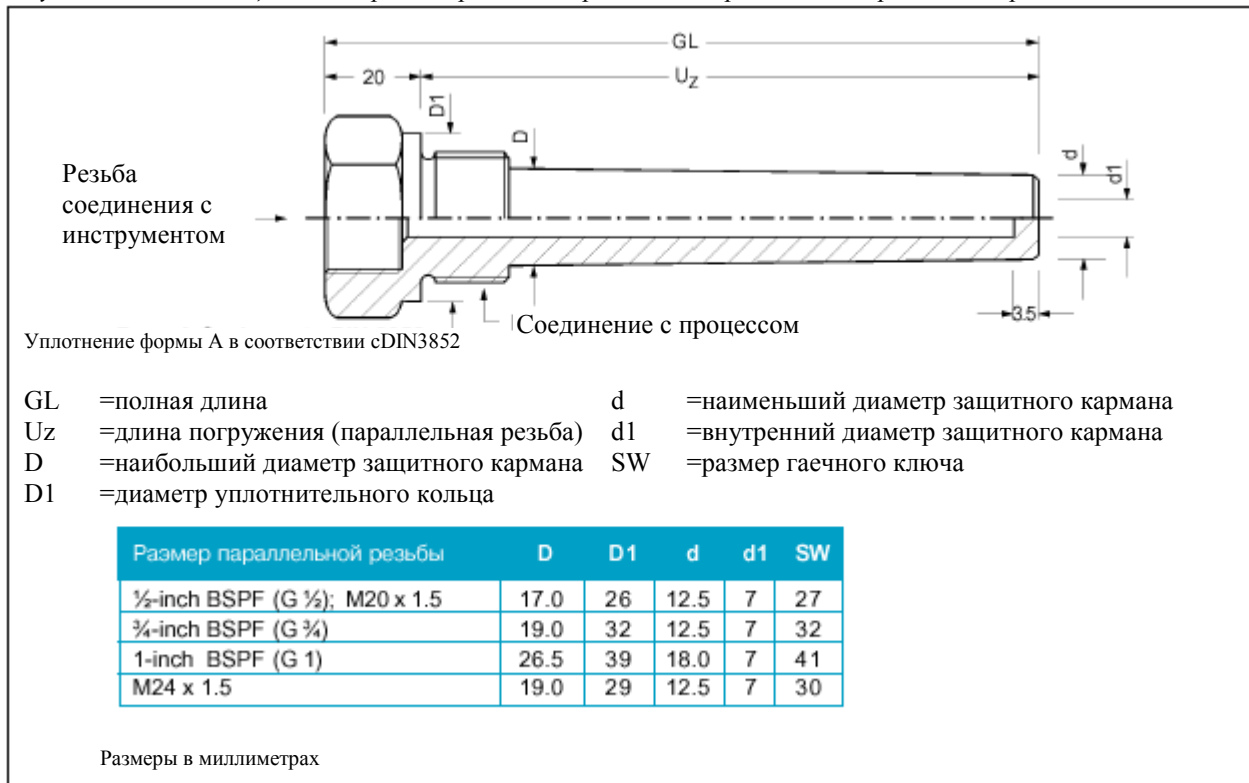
Литой защитный карман серии 96 для резьбового крепления с трапециевидной резьбой
